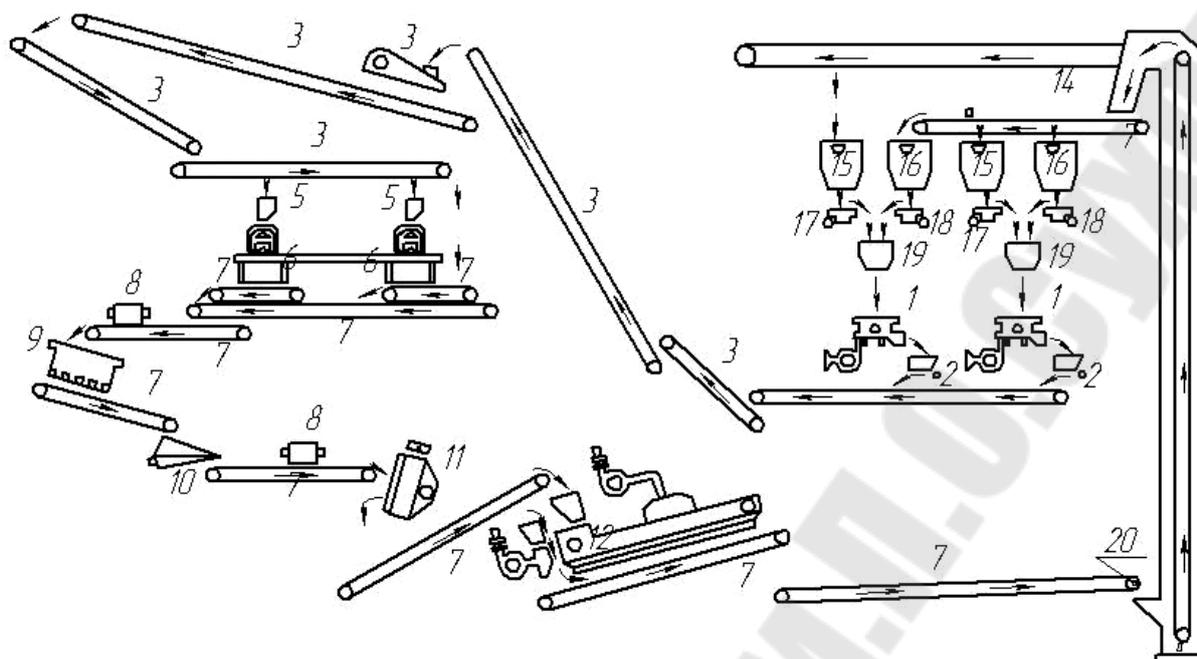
Схема типовой смесеприготовительной системы для автоматической линии опочной формовки чугунного литья:
